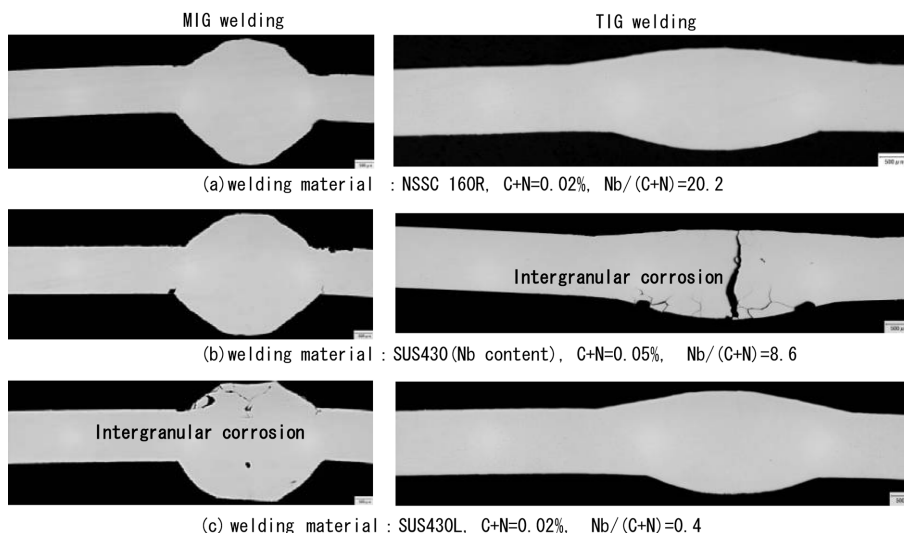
SUH409鋼板の各種溶接材料を用いた突き合わせ溶接部(MIG, TIG)の粒界腐食試験(改良strauss試験, JIS G 0575, 硫酸:0.5%, 硫酸銅:5%)後の粒界腐食状況(断面埋め込み研磨面) Intergranular corrosion circumstance of the welds (MIG & TIG) after Intergranular corrosion test (modified Strauss test, JIS G 0575, H₂SO₄: 0.5%, CuSO₄: 5%)
